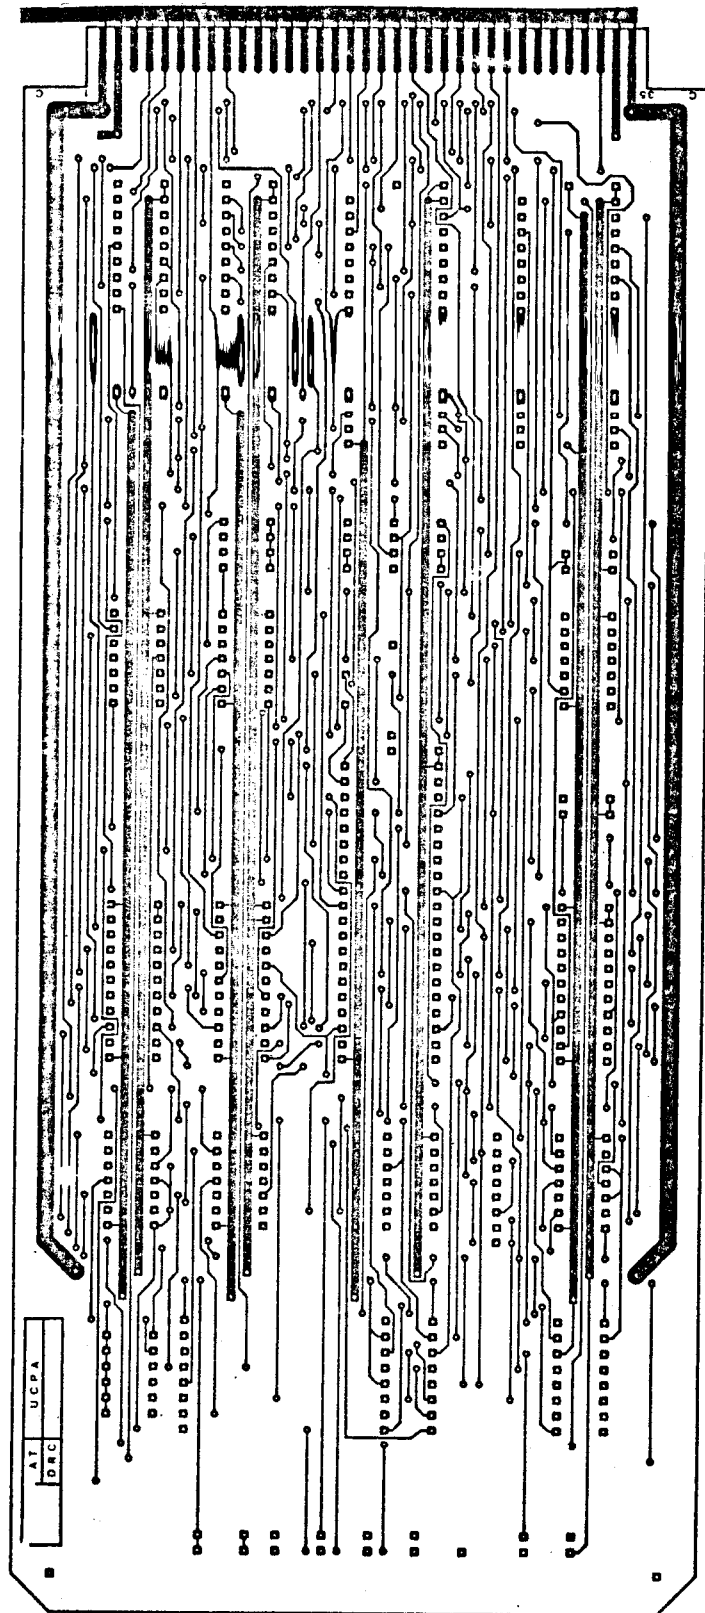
"Lay-out" da placa do circuito impresso (lado dos componentes).
